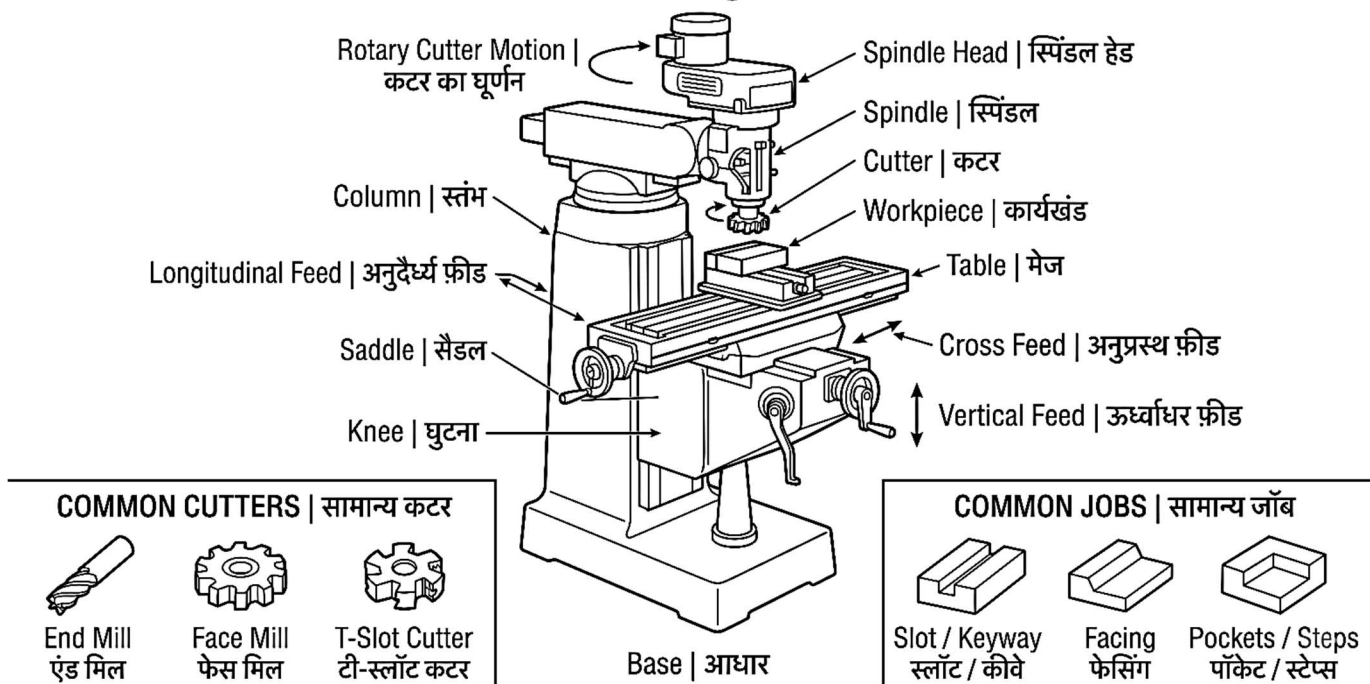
Vertical Milling Machine | वर्टिकल मिलिंग मशीन
